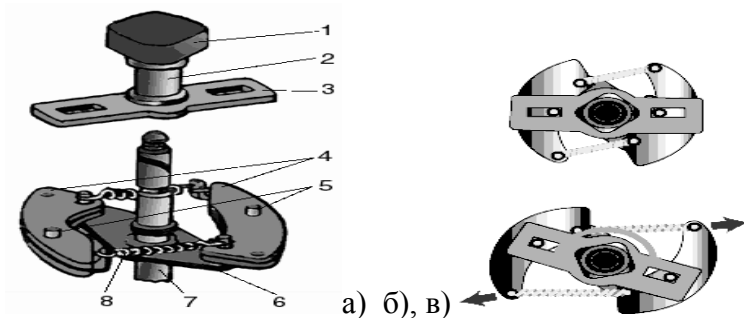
Схема работы центробежного регулятора угла опережения зажигания: 1 - кулачок прерывателя; 2 - втулка кулачков; 3 - подвижная пластина; 4 - грузики; 5 - шипы грузиков; 6 - опорная пластина; 7 - приводной вал; 8 - стяжные пружины. а) расположение деталей регулятора б) грузики вместе в) грузики разошлись
